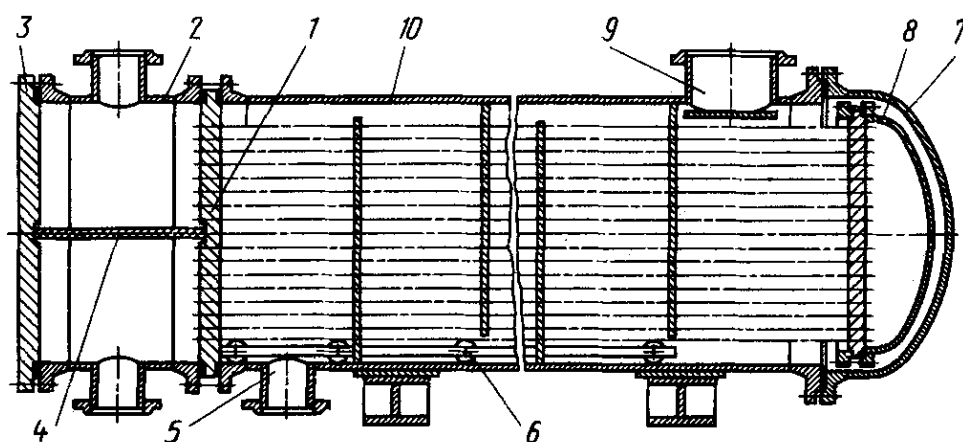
Горизонтальный двухходовой конденсатор с плавающей головкой
